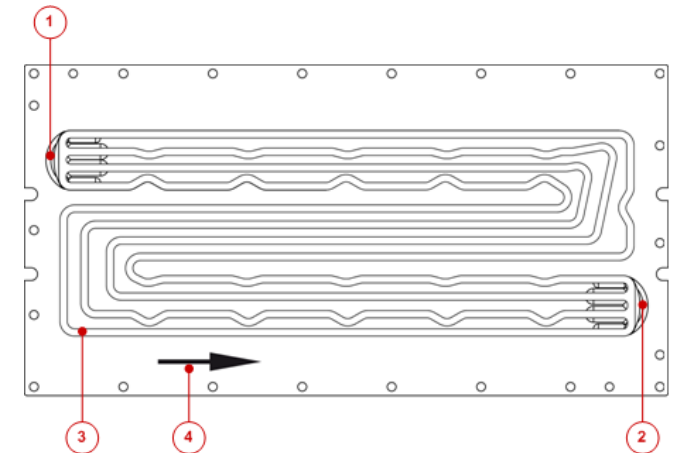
Kühlplatte von unten / Cooling plate bottom side
